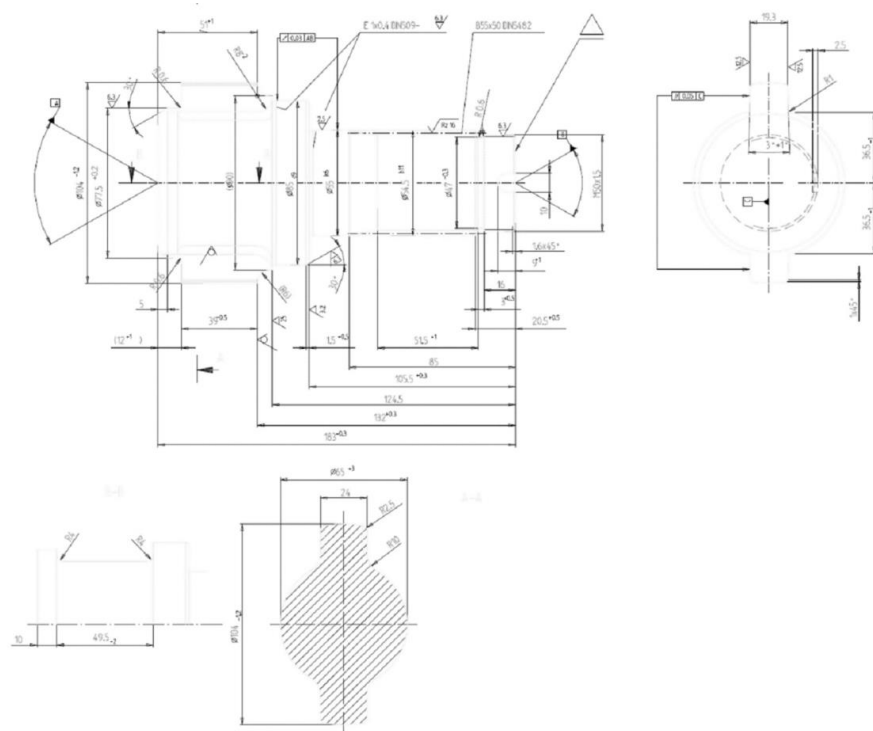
Проміжний вал приводу циліндричної шестерні
